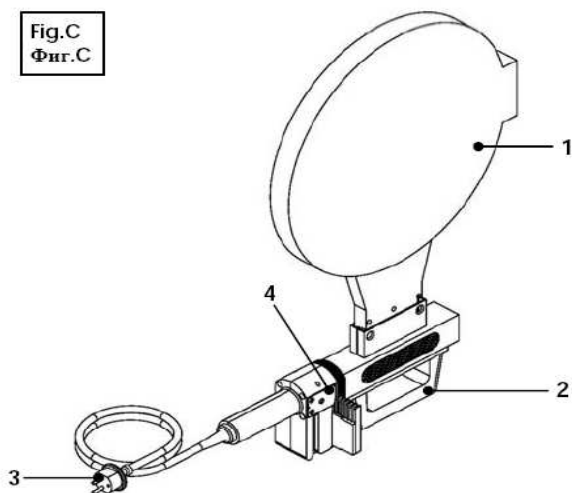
termoplaca, 2- maner, 3- cablu de alimentare, 4- termostat
